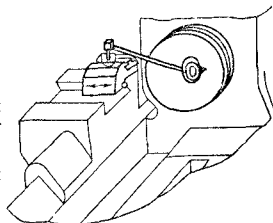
Проверка перпендикулярности перемещения суппорта к оси шпинделя у револьверного станка при помощи устанавливаемого диска.
